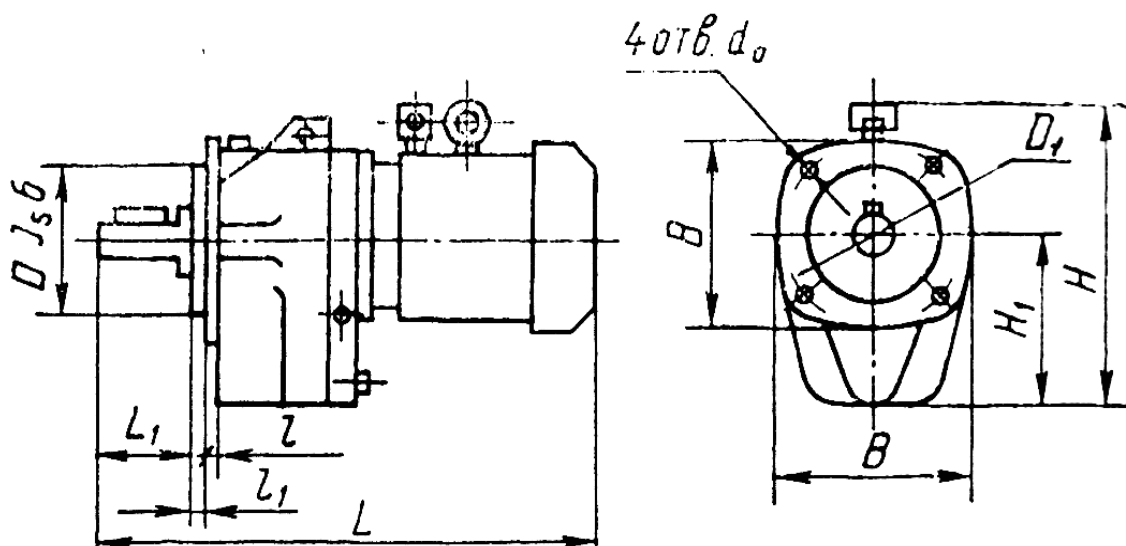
П6 Габаритные и присоединительные размеры мотор-редуктора с фланцем
